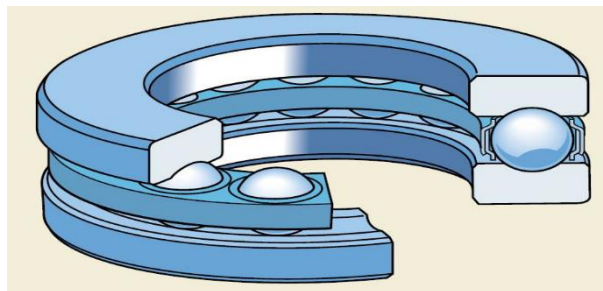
Конструкція кулькового упорного підшипника
